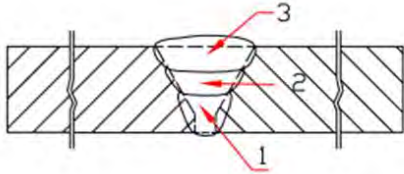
Cordones de soldadura 1 electrodo 6010, 2 y 3 electrodo 7018.
